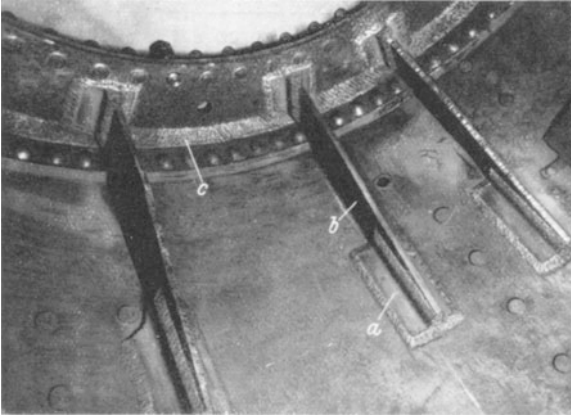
Verstärkungsanker an einem geschweißten Krepfenbruch.
